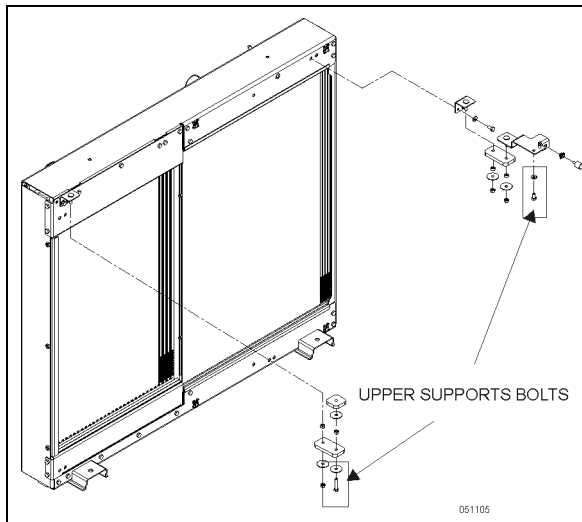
TORNILLOS DE MONTAJE DE SOPORTES SUPERIORES
